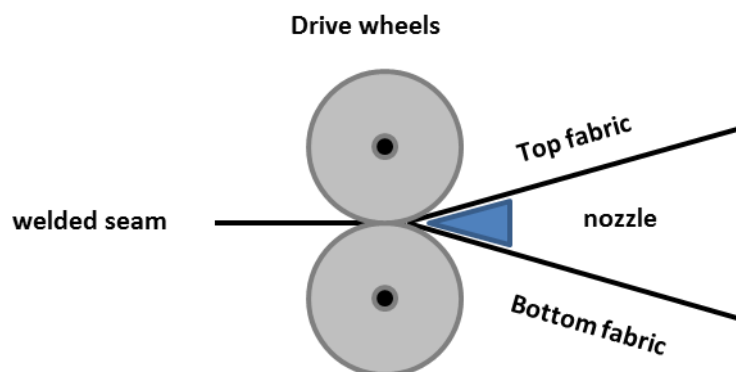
Einlegen des Gewebes im Schweisskopf
